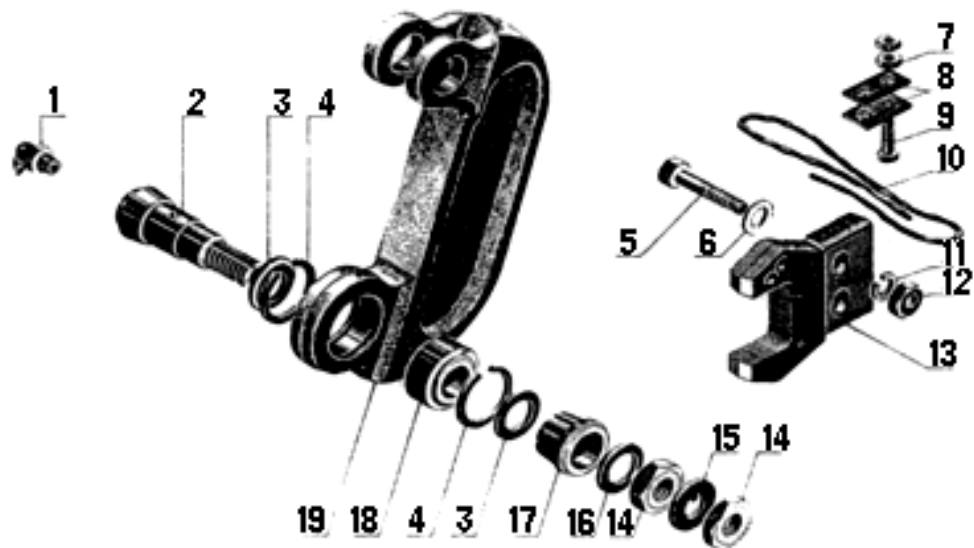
Підвіска тягового редуктора (нижня частина):
